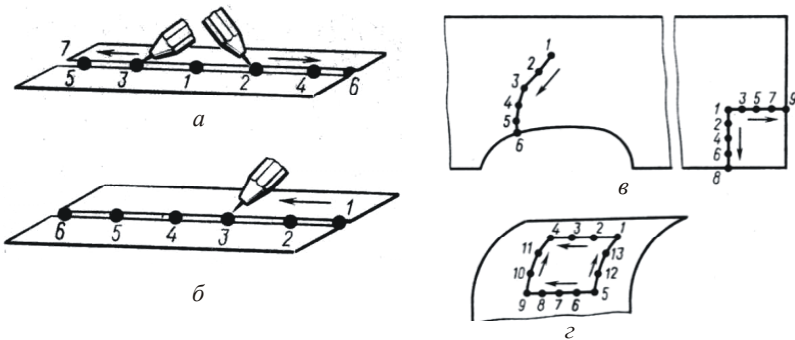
Последовательность расположения точек сварки:
